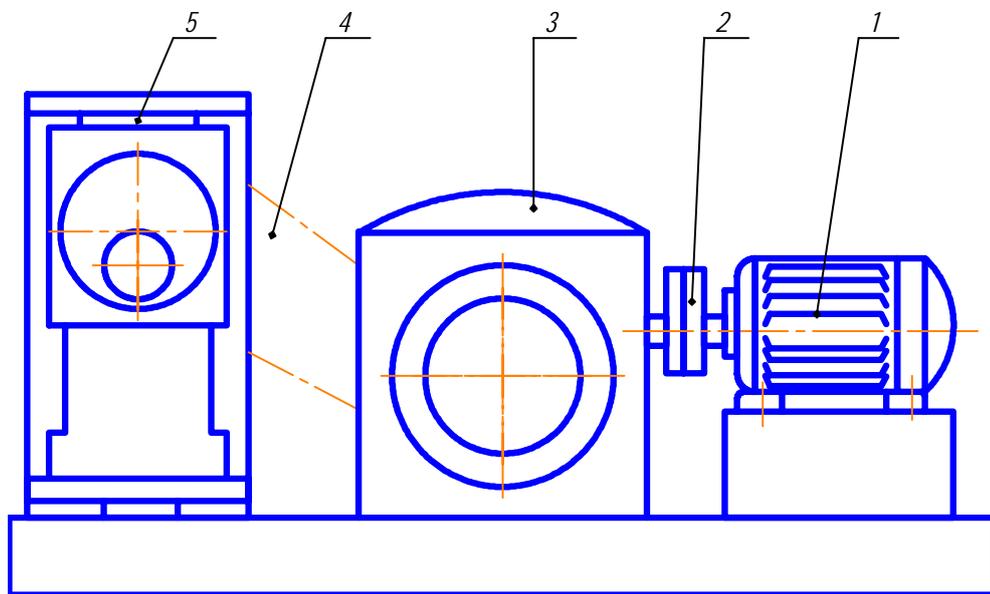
Загальний вигляд лабораторної установки для дослідження статички виконавчого механізму
